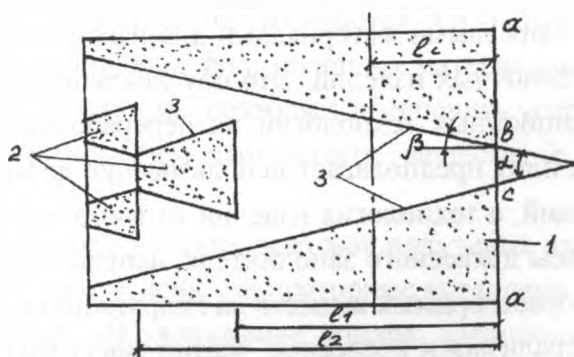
Развертка рабочей поверхности секторных выступов ролика:
